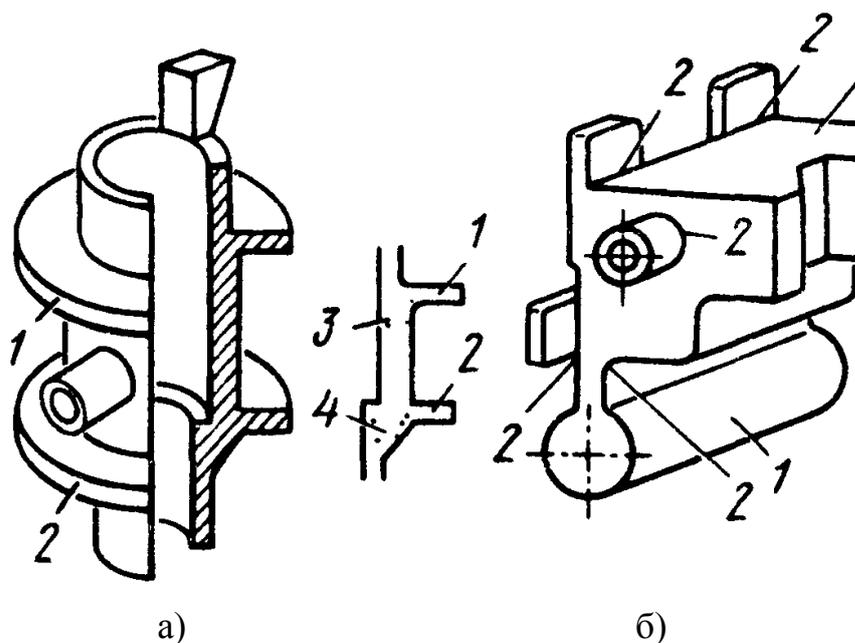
Нетехнологические конструкции отливок втулки (а) и корпуса (б) из алюминиевого сплава
